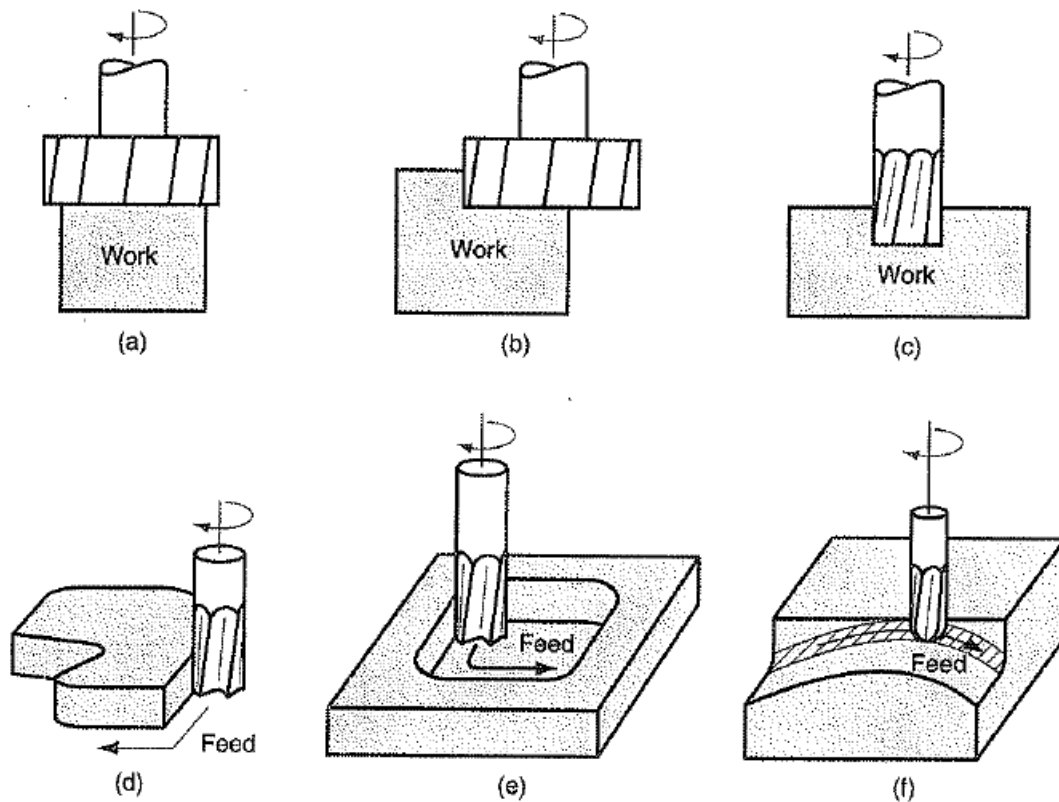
Fresagem de topo: a) faceamento, b) faceamento parcial, c) fresagem frontal de canal, d) fresagem lateral de contorno, e) fresagem de caixa, e f) fresagem de superfície 3D [22].
